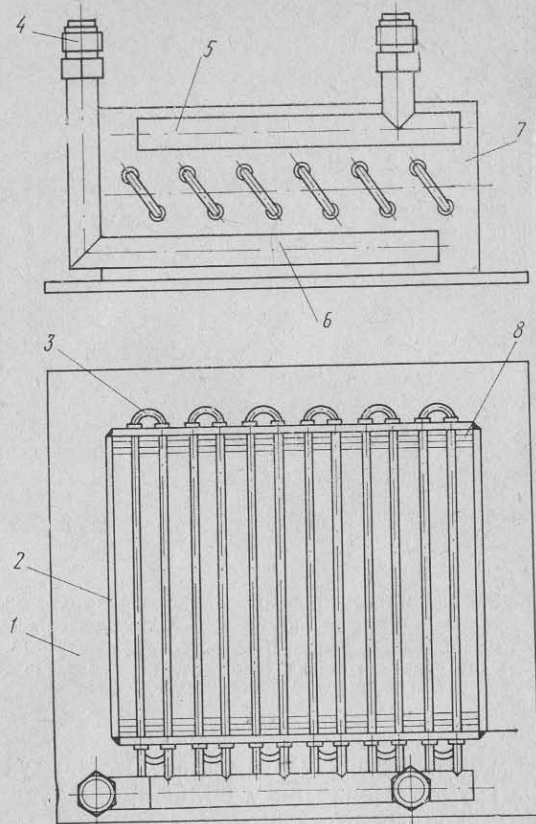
Общий вид многоходового воздушонагревателя с калачами
